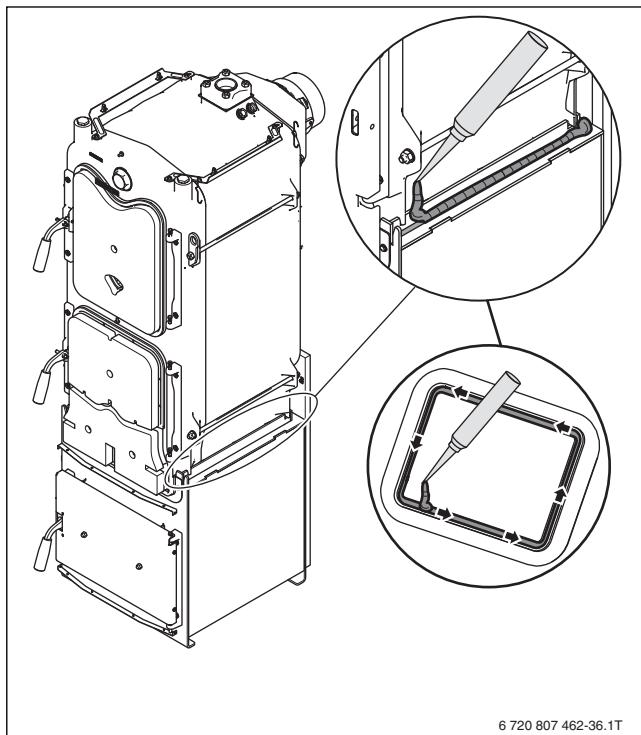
Уплотните соединения между корпусом котла и топочной камерой
